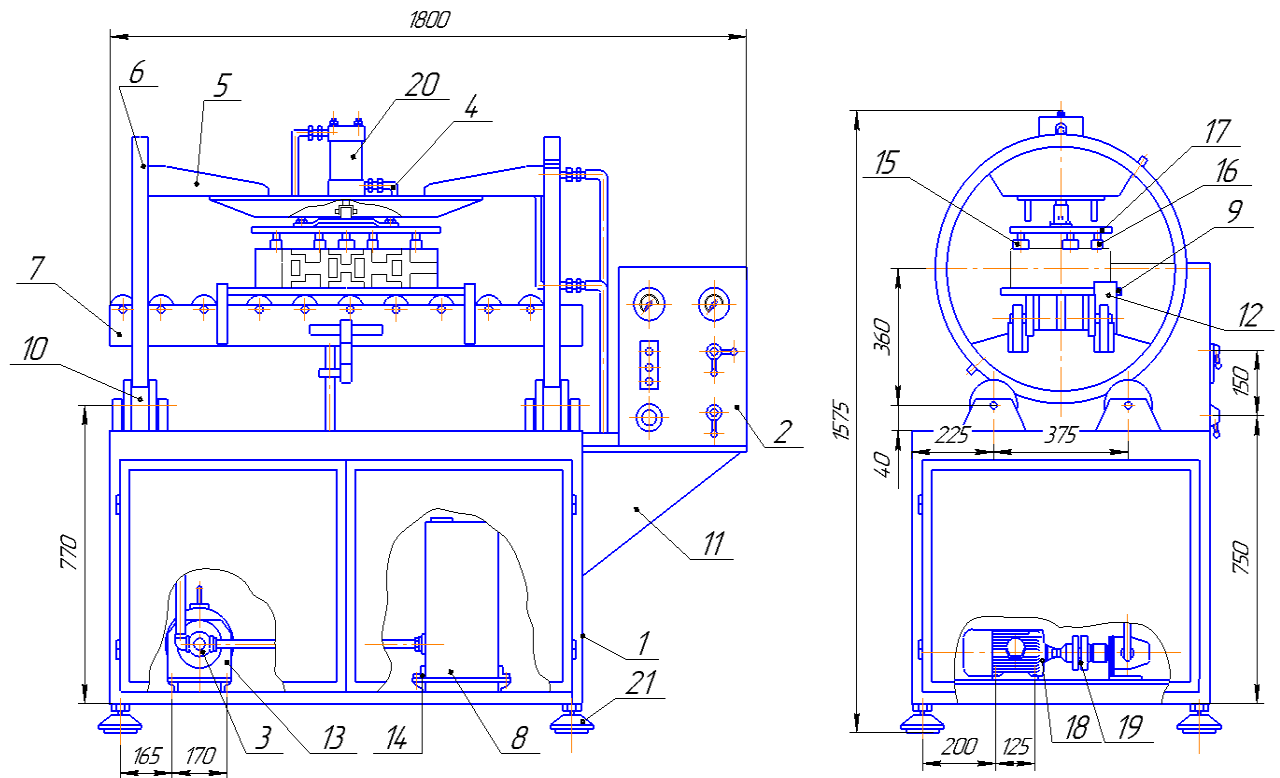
Загальний вид конструкції стенда: 1 – Каркас; 2 – Пульт керування;
